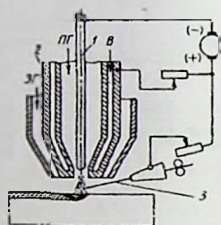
Плазменно-порошковая наплавка с токоведущей присадочной проволокой:
